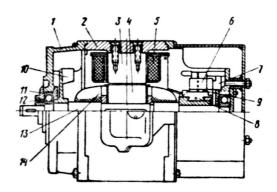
Электродвигатель $S7/5 \times 2$ механизма регулировки числа оборотов дизеля и независимого возбуждения главного генератора: I—подшипниковый щит: 2—остов; 3—сердечник главного полюса: 4—сердечник якоря; 5—катушка главного полюса: 6—щеткодержатель; 7—кольцо; 8—коллектор; 9—щетка; 10—вентилятор; 11—шарикоподшипник; 12—крышка подшипника; 13—вал якоря; 14—обмотка якоря
